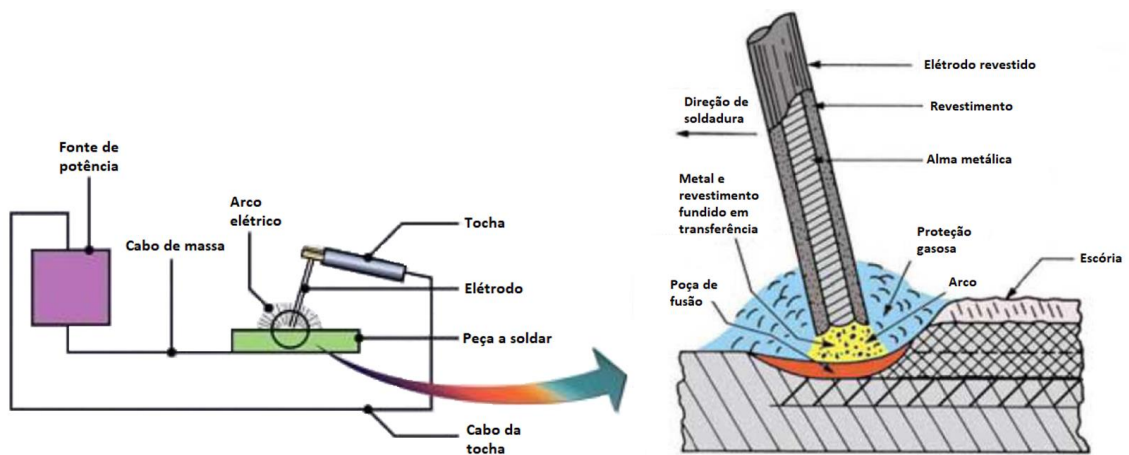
Esquema de soldadura eléctrodo revestido [19]
